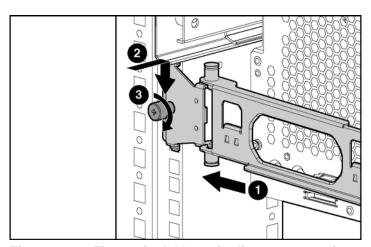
Fissaggio del braccio di supporto cavi al rack a fori quadrati
